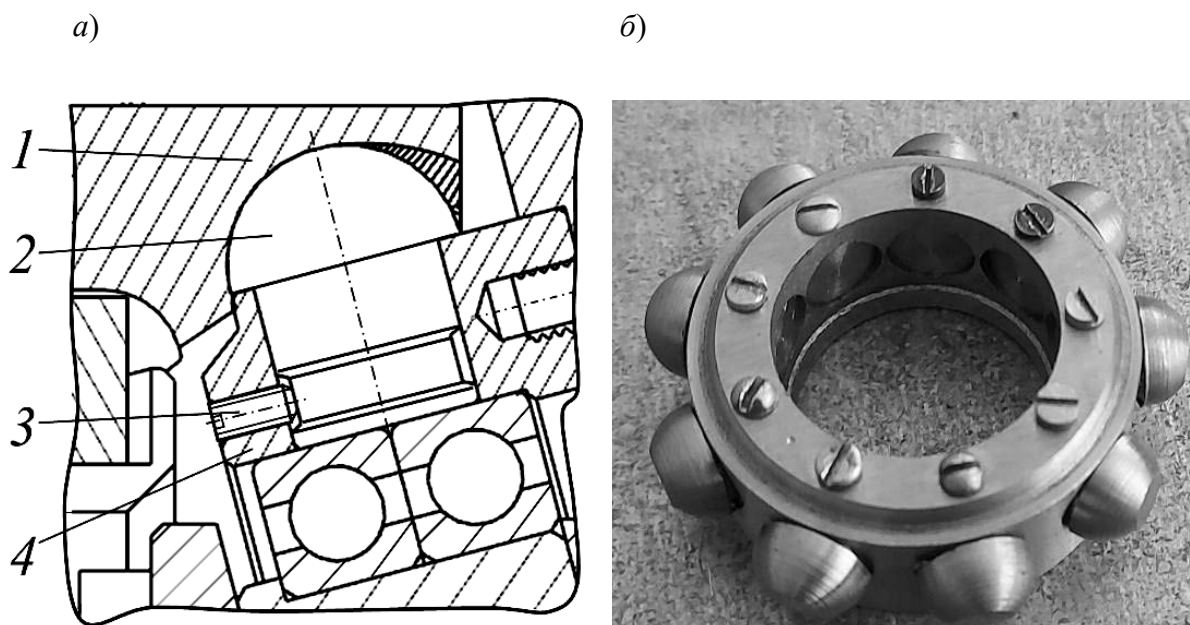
Механизм фиксации ролика: *а* – конструктивная схема; *б* – изготовленный образец внутренней части сателлита
